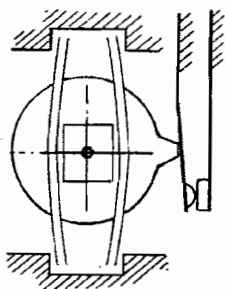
Механизм кулачкового типа выключателя (переключателя).
